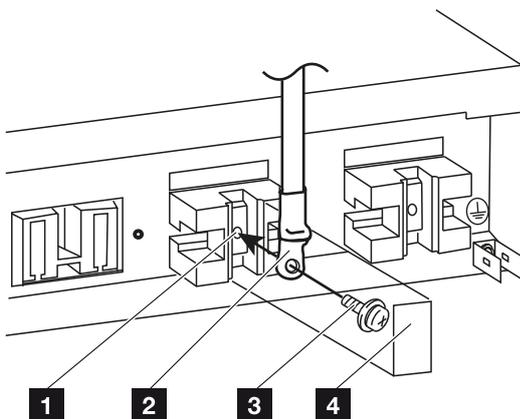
Anschluss DC-Leitung Switch Box - Controller BMU
